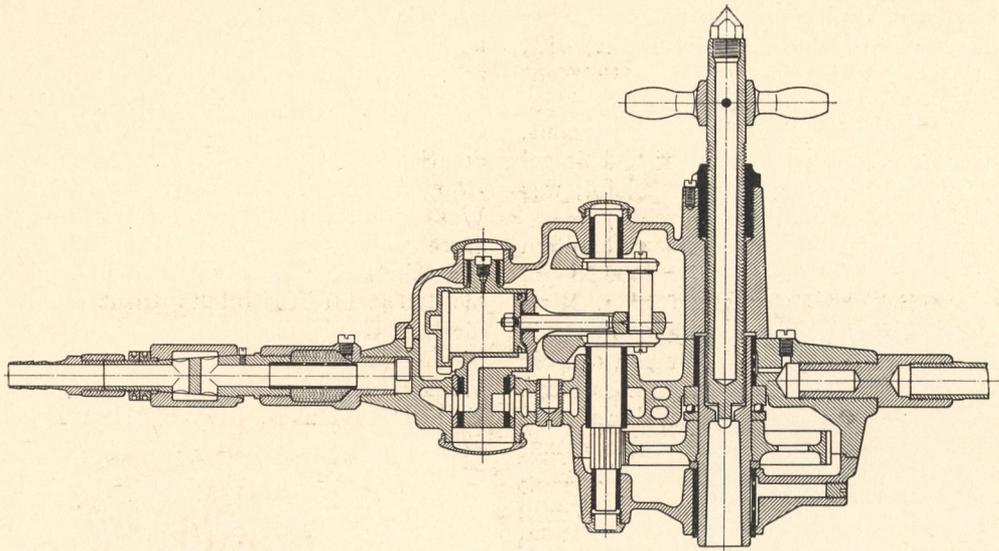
Transportable Preßluftbohrmaschine. Bauart: W. Kühn.
